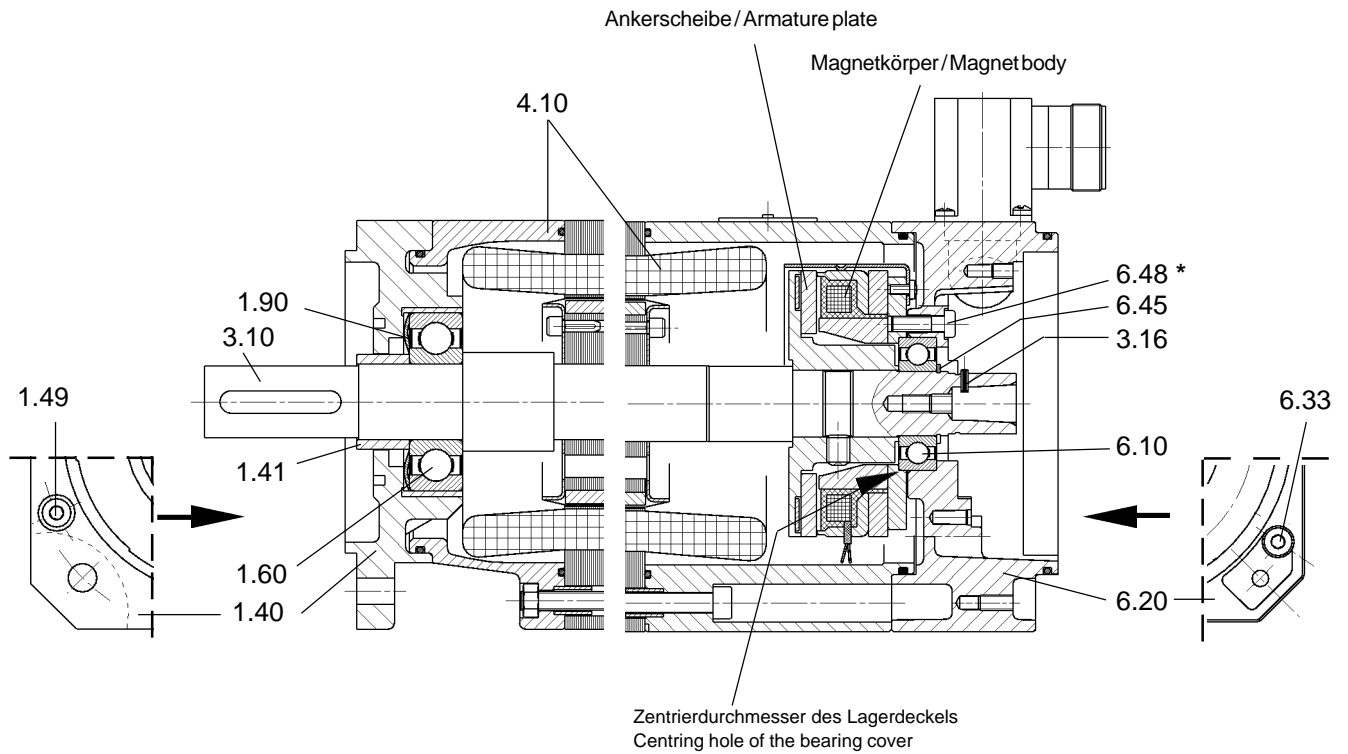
Demontage/Montage von Motorläufer / Removing/Fitting motor rotor
